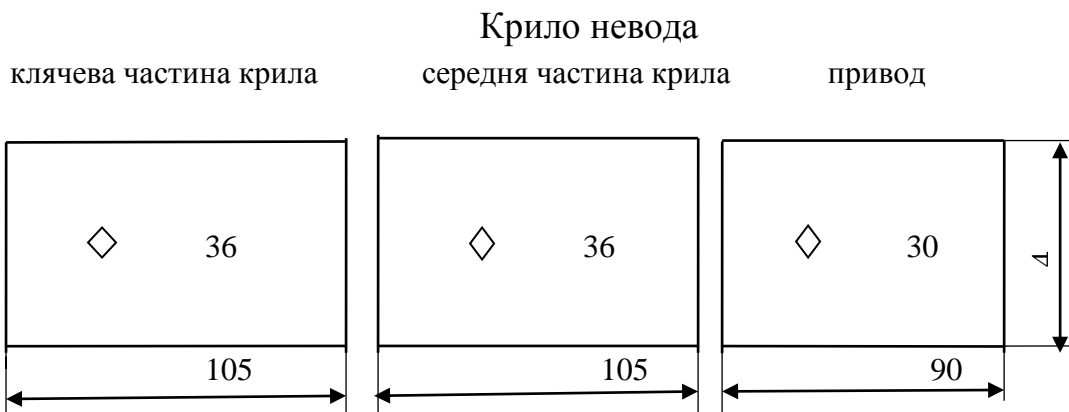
Невід закидний 605×6 для вилову товарної риби
